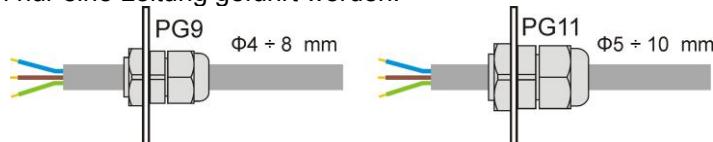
Die empfohlenen Durchmesser der Anschlussleitungen für die Kabelverschraubungen PG9 und PG11.
